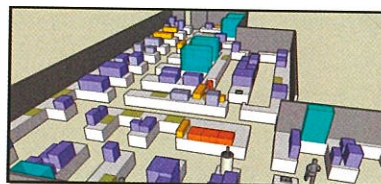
Plano de Piso del Laboratorio 1 (Vista 3)
